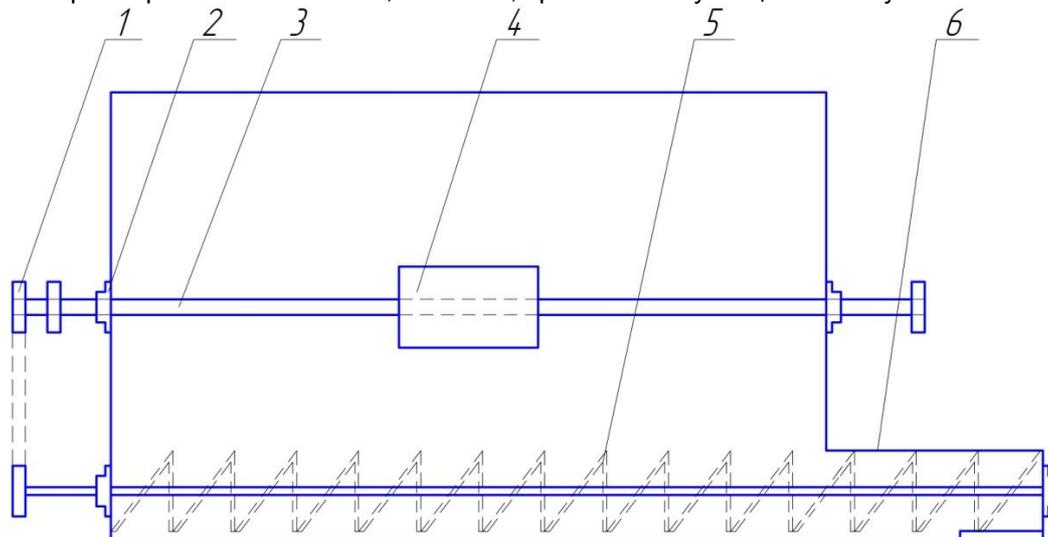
Кормопогрузчик с выгрузным шнеком: 1. Ведущая звездочка 2. Подшипник 3. Вал 4. Редуктор 5. Шнек 6. Корпус шнека
